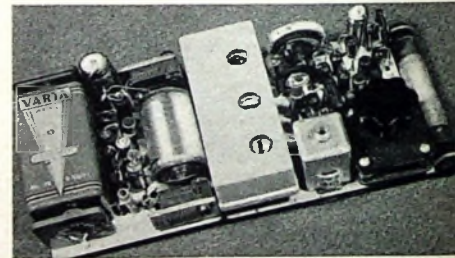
Gesamtansicht des Minisuper mit dem 1,5-W-Verstärker
